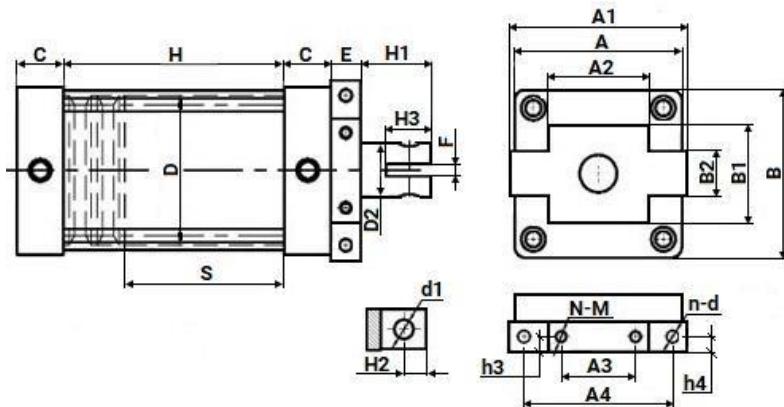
Размеры пневмоцилиндра SC 100x120
